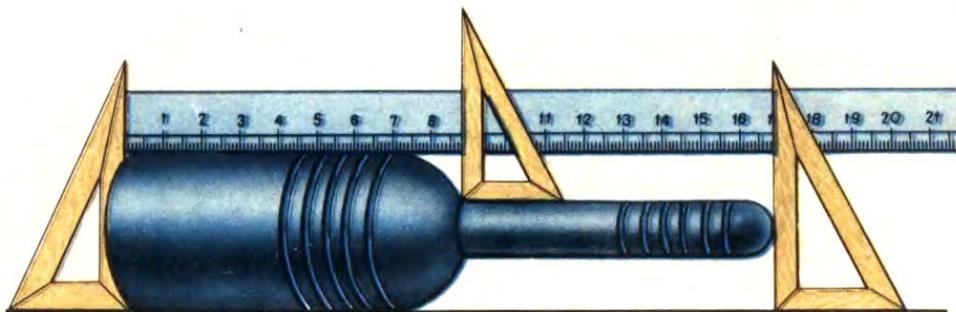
Вимірювання довжини деталі, що має ступінчасту форму
